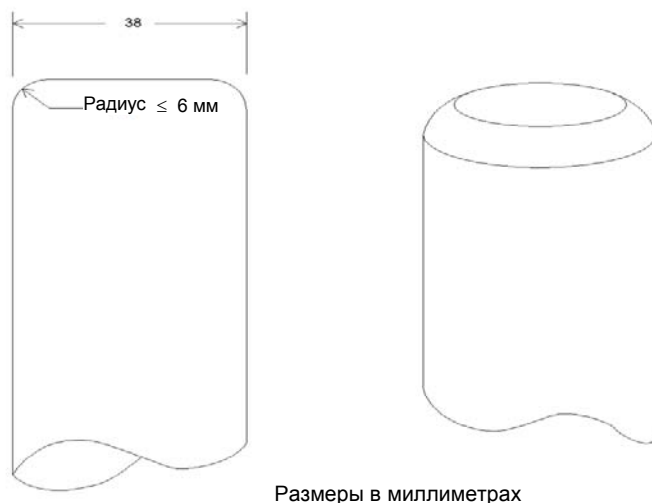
Цилиндрический стальной стержень, используемый при испытании на пробивание
